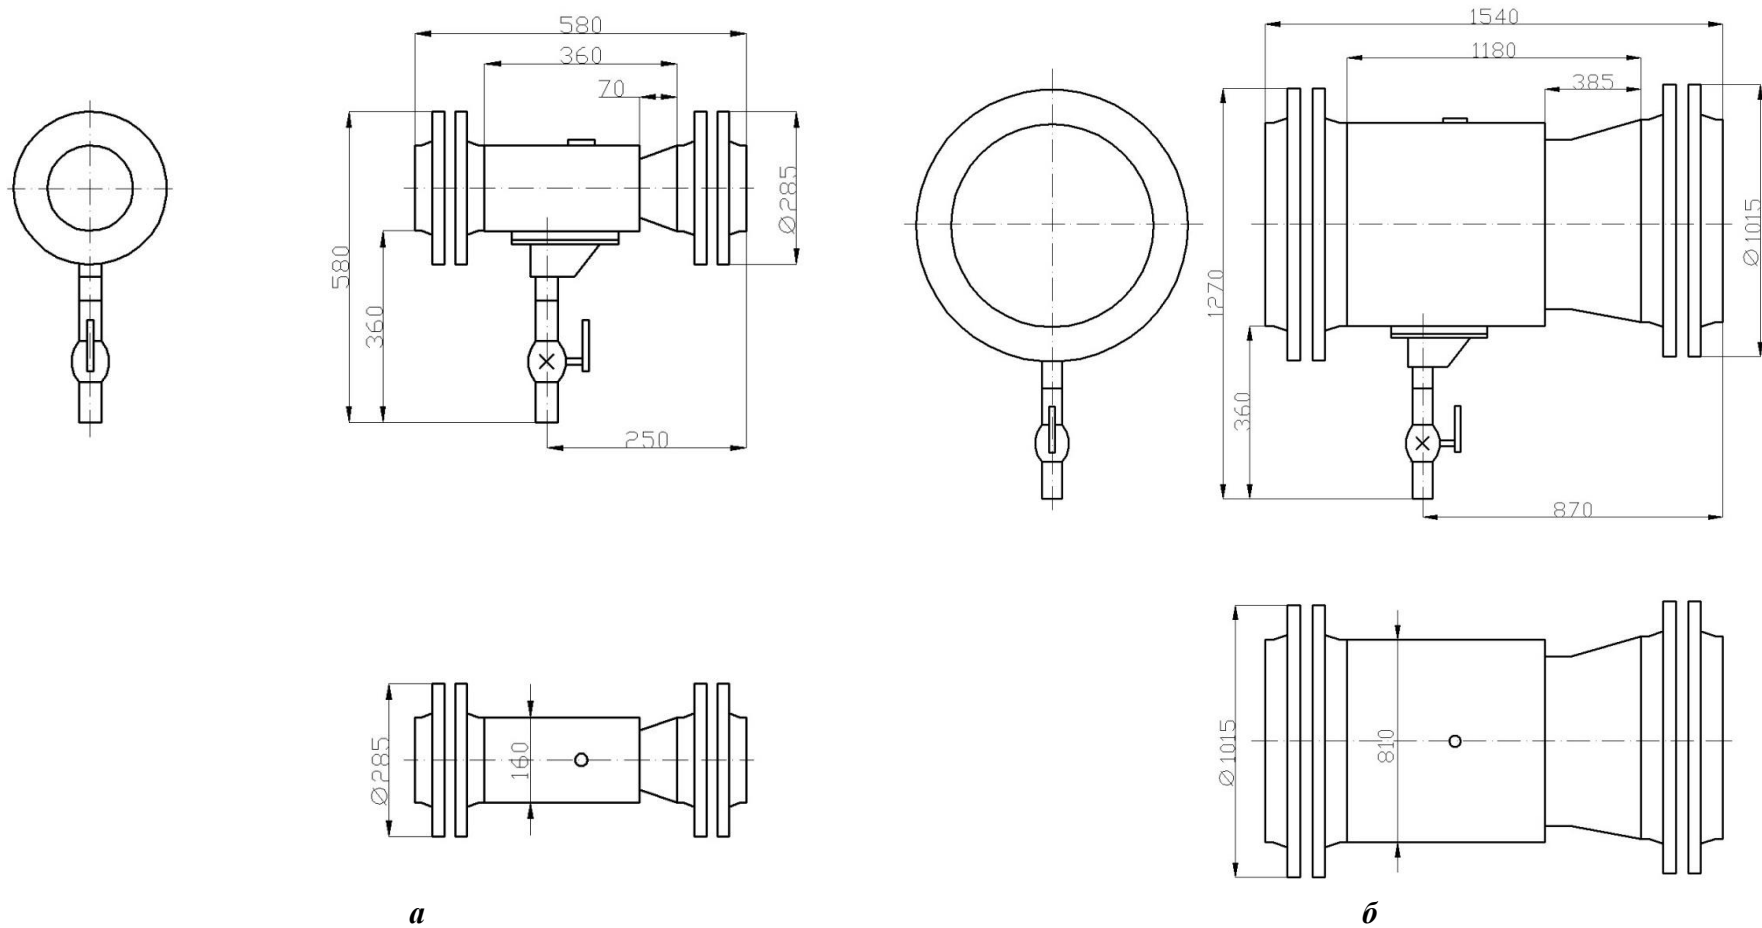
Габаритные размеры пробоотборника типа «ПЦП»
